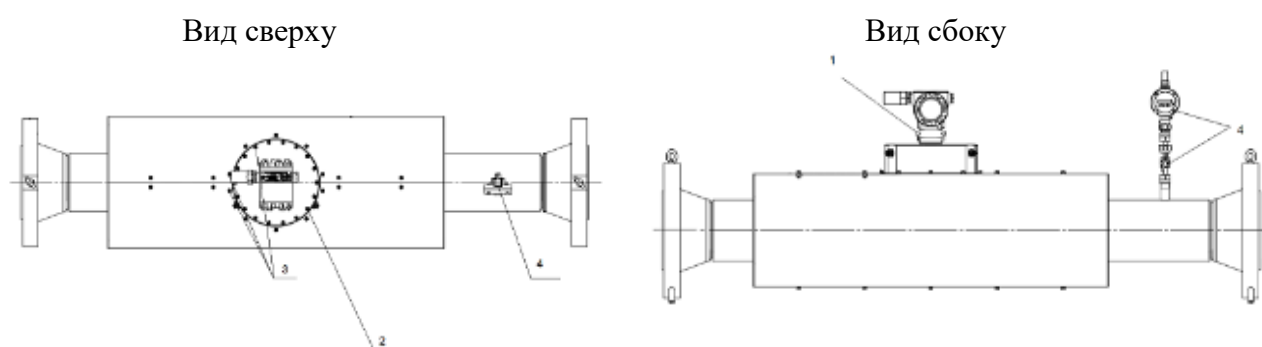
Корпус круглого сечения с защитным кожухом
